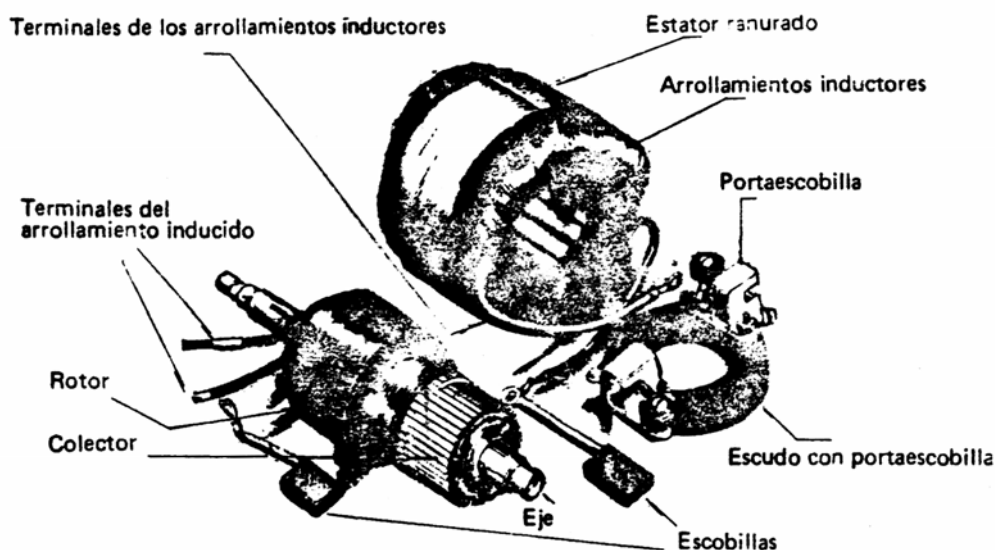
PARTES COMPONENTES DE UN MOTOR UNIVERSAL.
